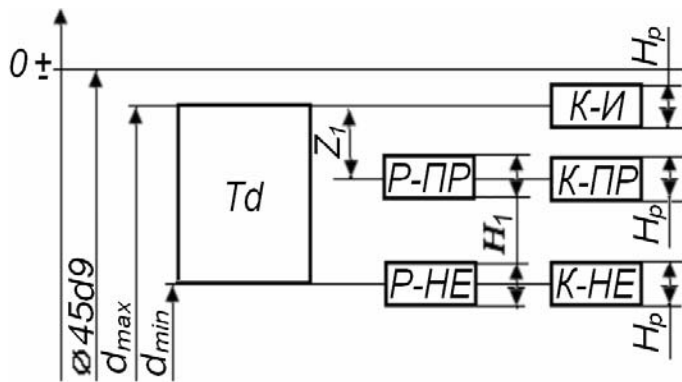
Схема розташування полів допусків контрольованого вала
